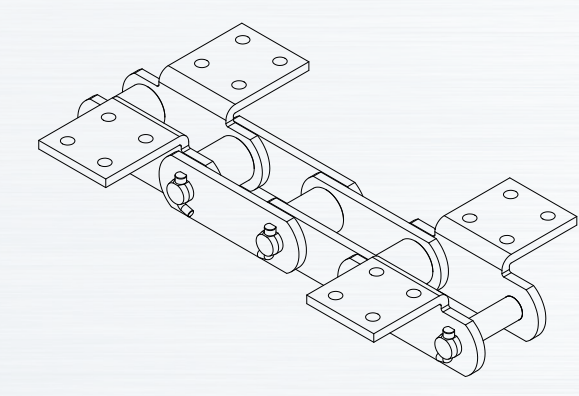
Cadena de placas rectas con rodillos pequeños
